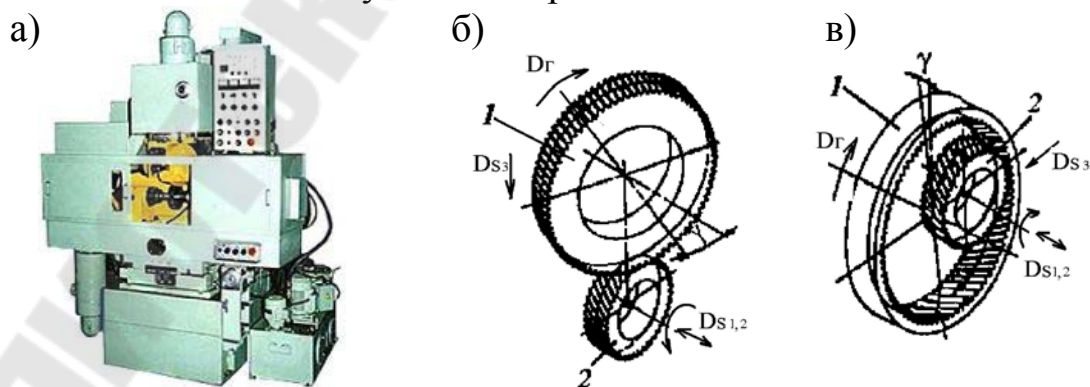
Общий вид зубохонинговального станка (а) и схемы обработки колес хонем с внешним (б) и внутренним (в) зацеплением: 1 – хон; 2 – зубчатое колесо
